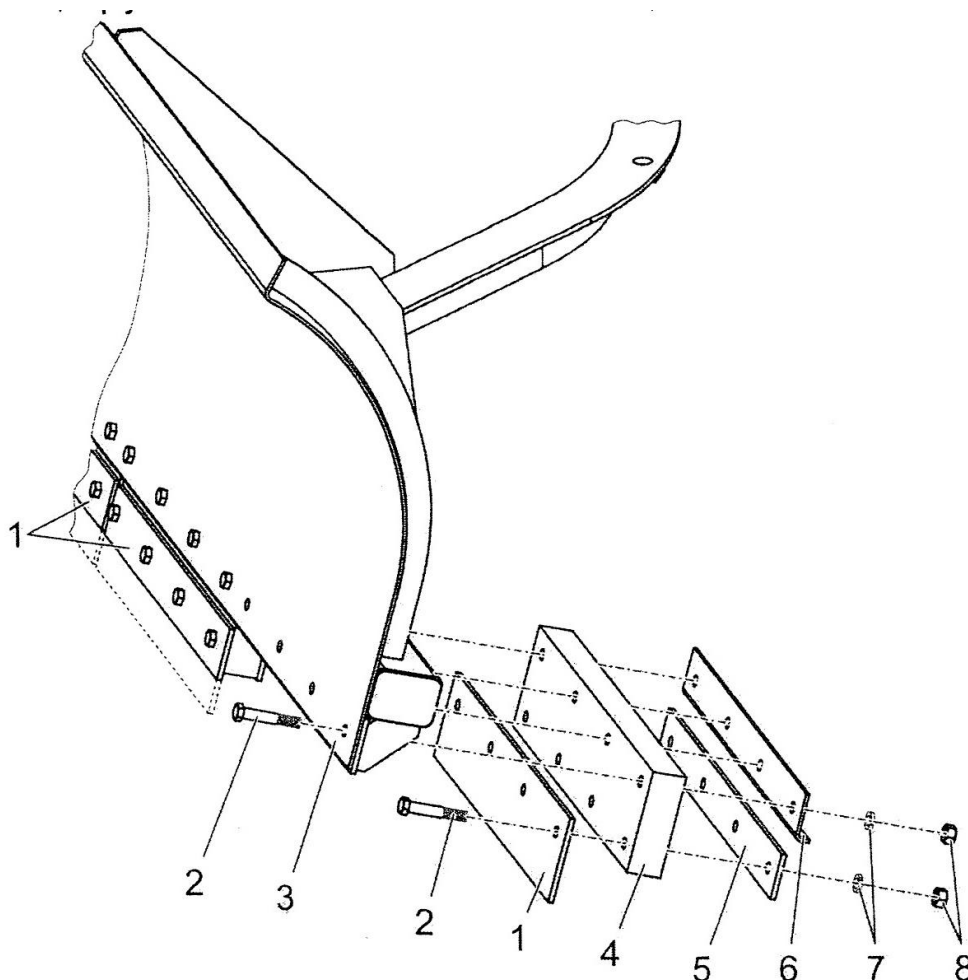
Крепёж ножей и амортизаторов отвала
